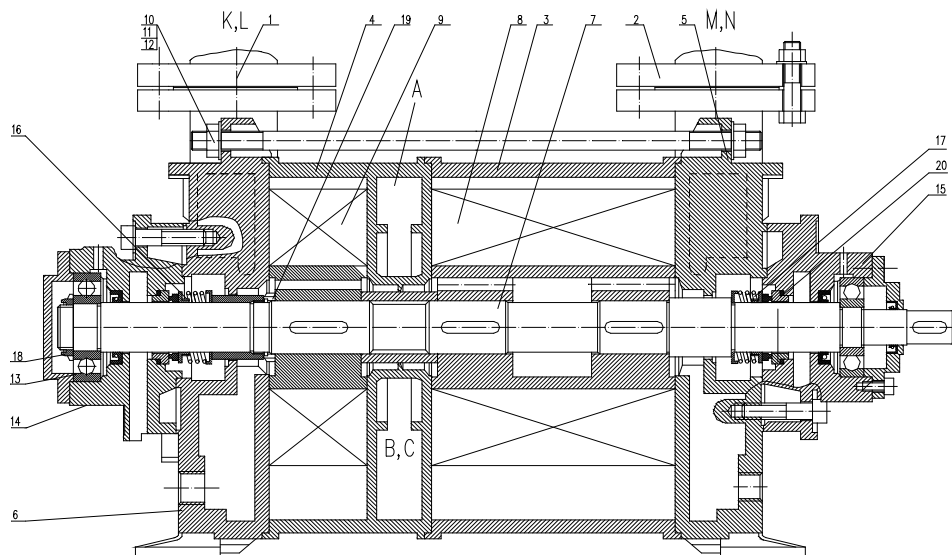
Конструкция двухступенчатого жидкостнокольцевого вакуум-насоса ЖВН ДМ 180: 1 – впускной патрубок; 2 – выпускной патрубок; 3 – корпус первой ступени; 4 – корпус второй ступени; 5 – торцовая крышка правая; 6 – торцовая крышка левая; 7 – вал; 8 – ротор первой ступени в сборе; 9 – ротор второй ступени в сборе; 10, 11, 12 – стяжки; 13 – шарикоподшипник; 14, 15 – корпус подшипника в сборе; 16, 17 – уплотнение осевое в сборе; 18, 19, 20 – стопорные и регулировочные гайки.
